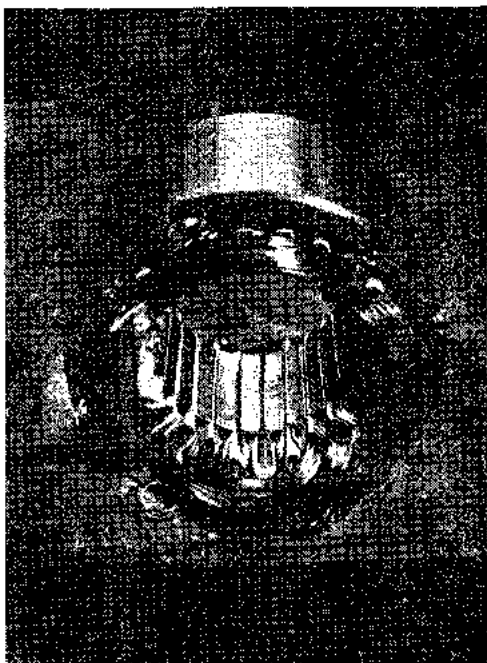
Dispunerea capetelor de bobină în părțile frontale ale înfășurării de sarcină a unui motor monofazat.
